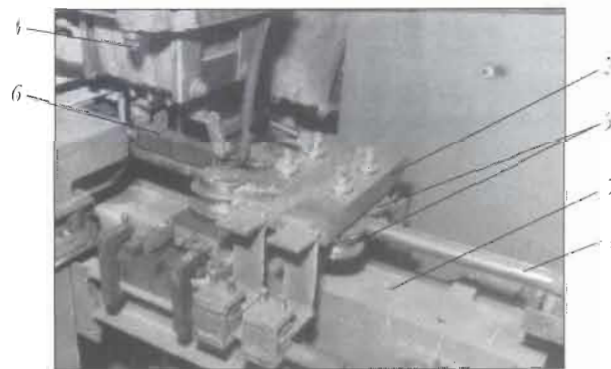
Лабораторное оборудование для проведения экспериментов: 1 — высокочастотный трансформатор; 2 — валковая клетка; 3 — две пары валков; 4 — свариваемая труба; 5 — станина; 6 — индуктор
